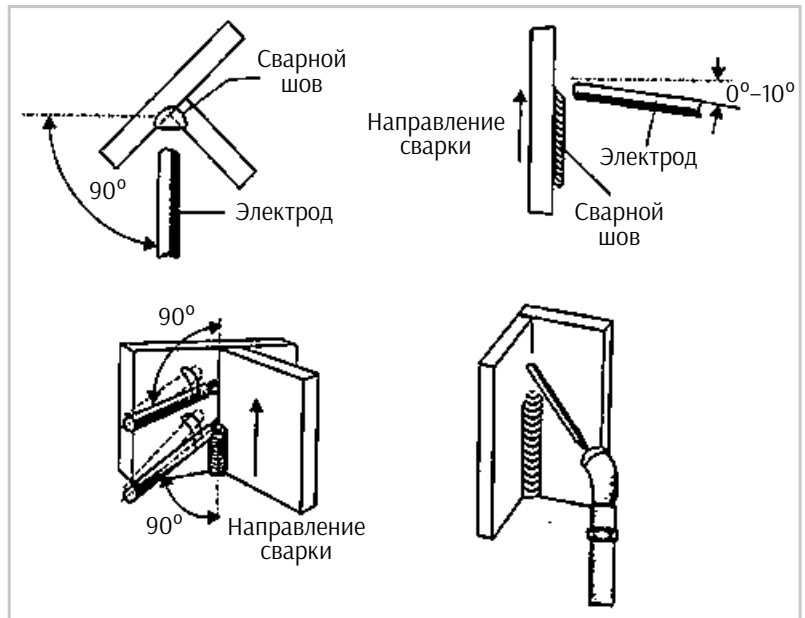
Положение электрода при сварке таврового соединения в вертикальном положении однопроходным угловым швом
